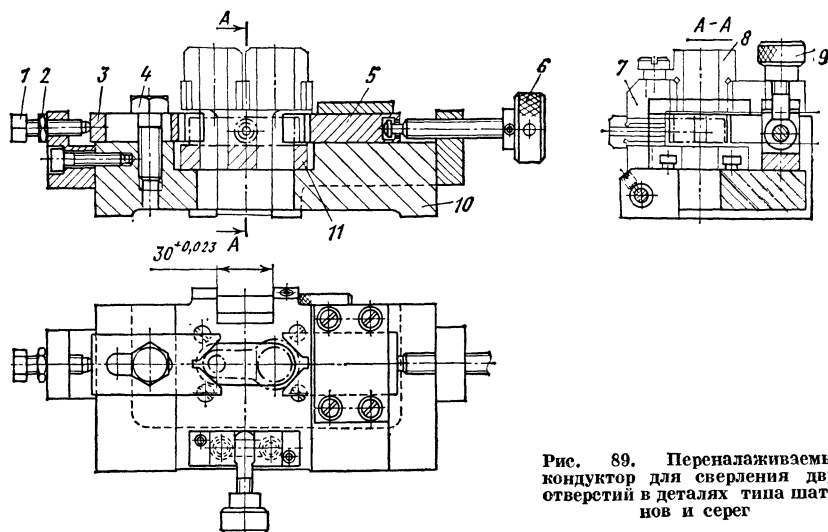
Переналаживаемый кондуктор для сверления двух отверстий в деталях типа шатунов и серег
